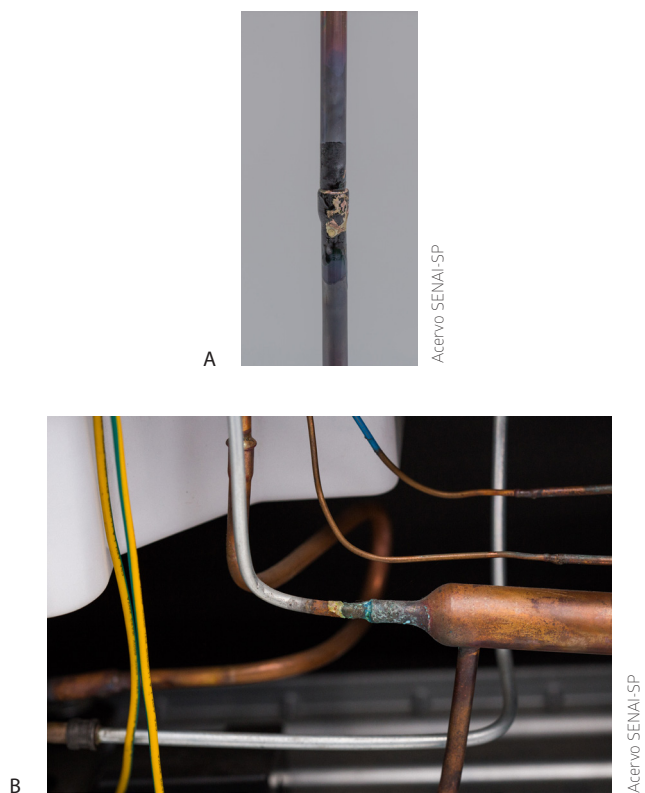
(A) Solda de cobre com cobre. (B) Solda de cobre com ferro.
